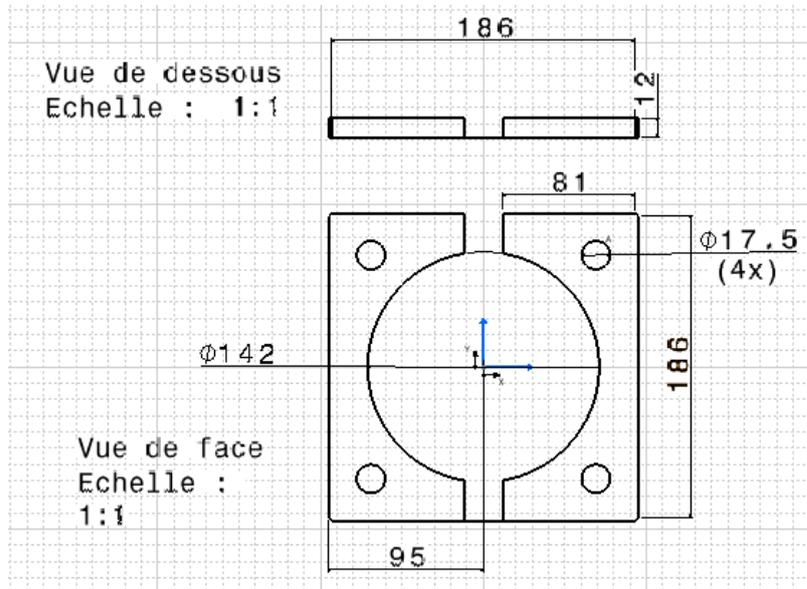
Dessin 2D de la plaque de fixation (DIVD)
